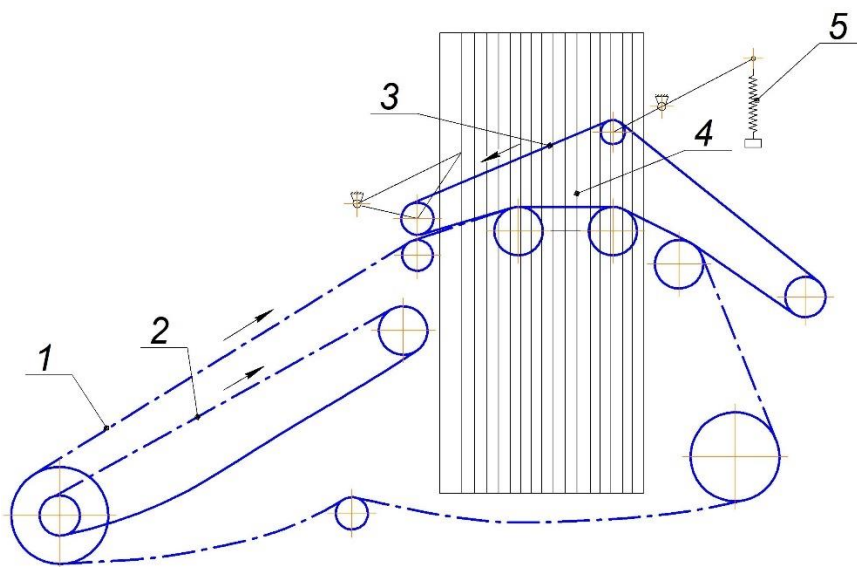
Бадиллєвидаляючий пристрій транспортерного типу
